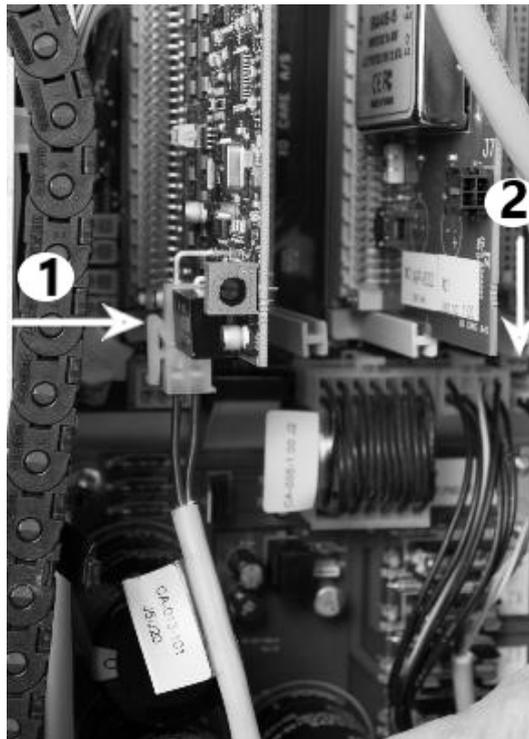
(1) CA-013 (J5, Stand control PCB), (2) CA-012 (J11, Backplane PCB)
